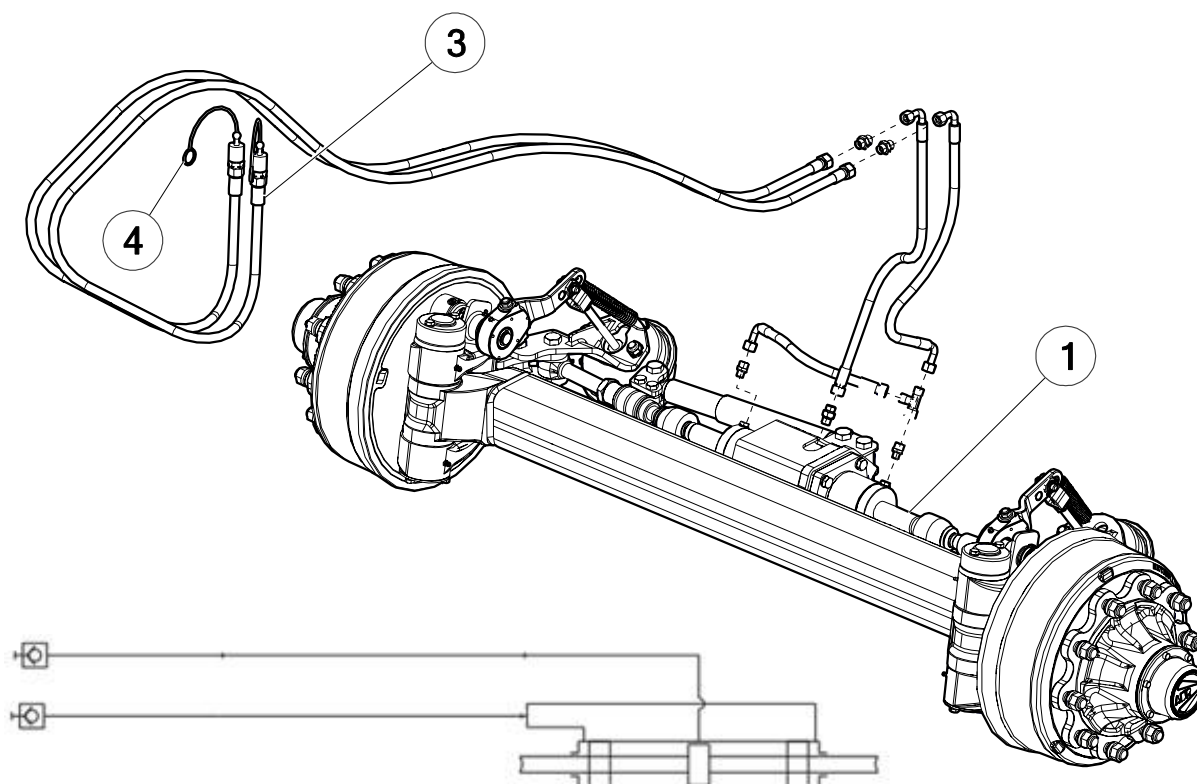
Схема установки гидравлической блокировки поворота задней оси
